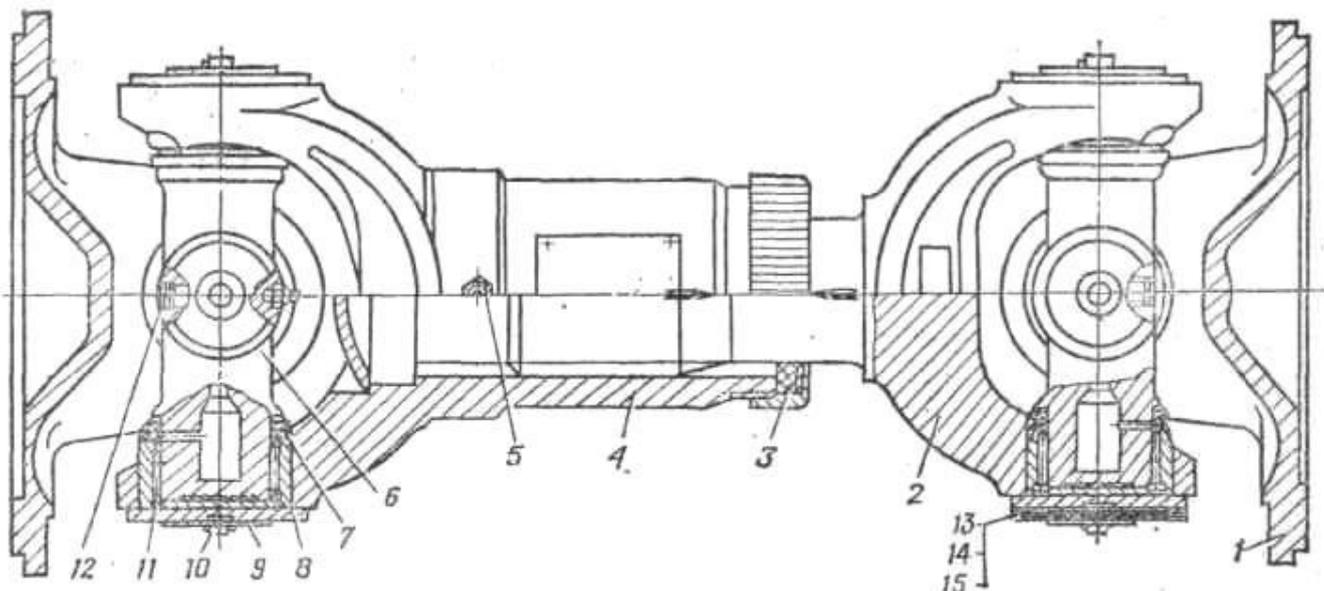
Промежуточный карданный вал с крестовинами и фланцами в сборе:
